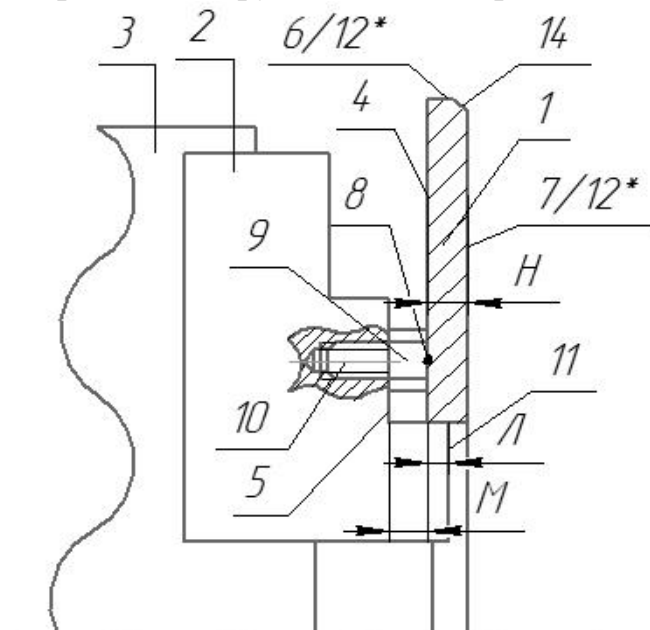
Схема базирования и закрепления заготовки детали «Фланец» с резьбовыми опорными шпильками.
